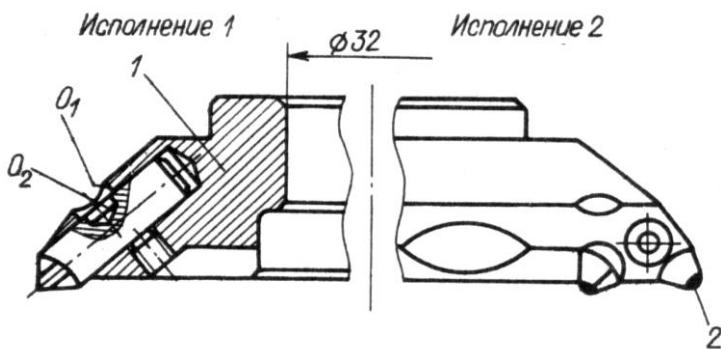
Фреза торцева насадна зі вставними ножами, оснащеними композитом, регульована
